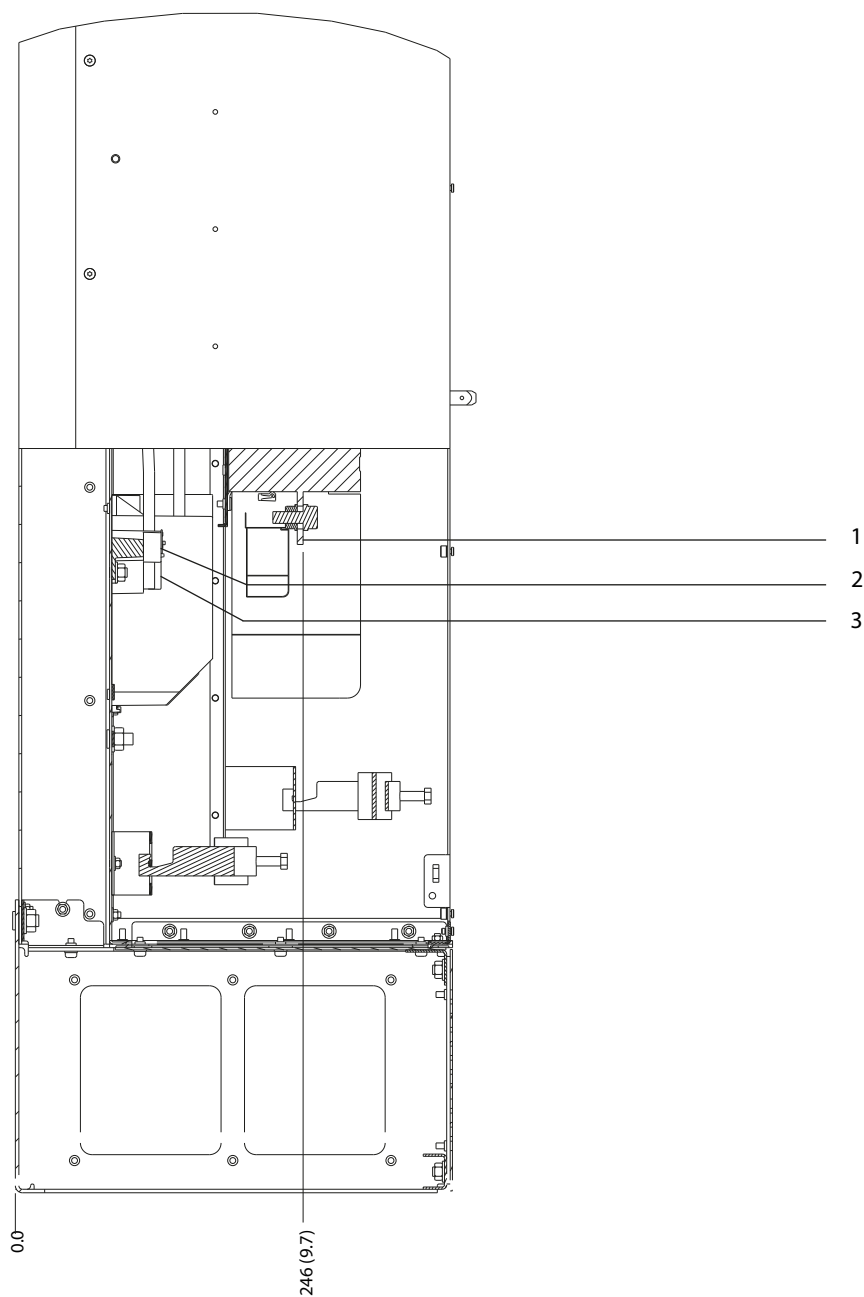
Dimensions des bornes D8h avec option contacteur (vues latérales)
